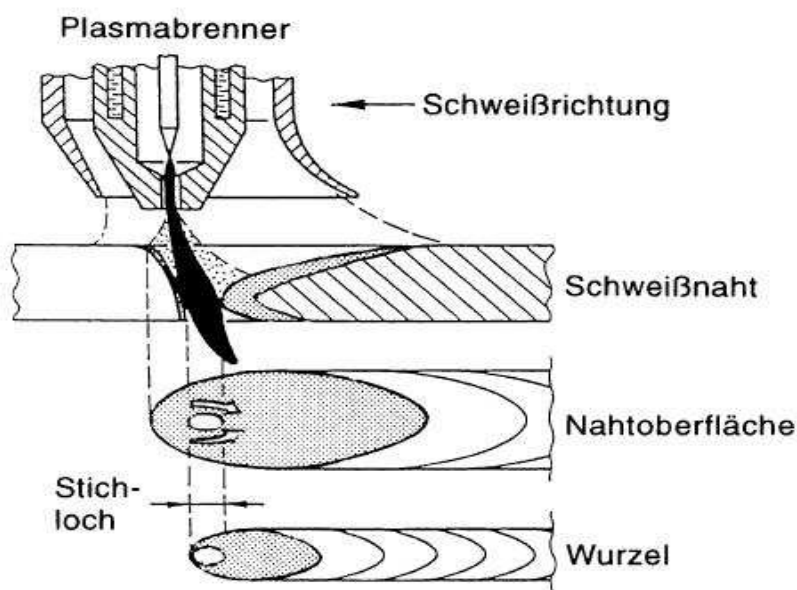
Schematische Anordnung beim Stichloch-Plasmaschweißen<sup>[ST01]</sup>
